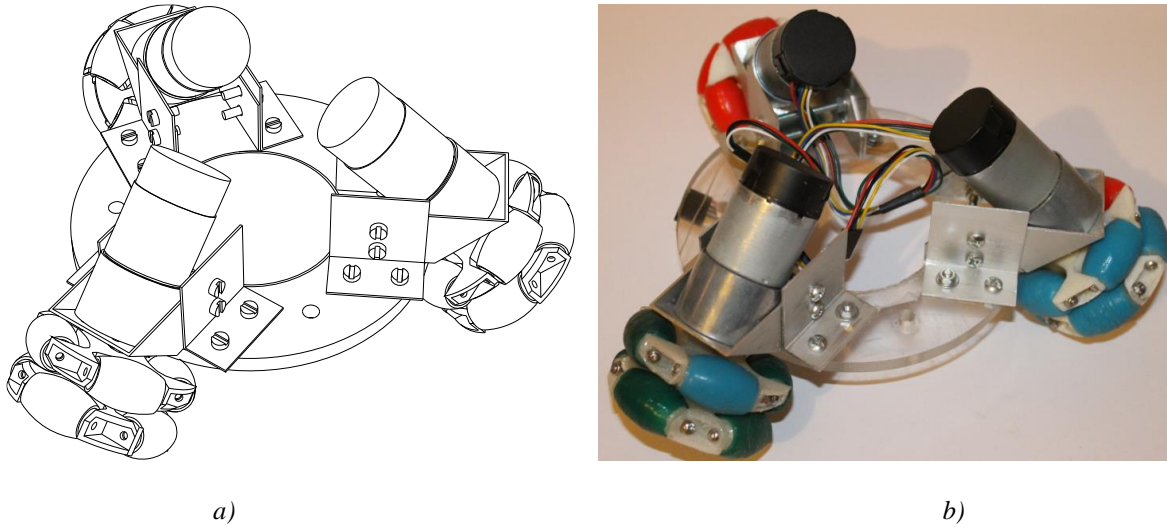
piso 0 robot ballbot UT. a) diseño CAD, b) construcción física.
